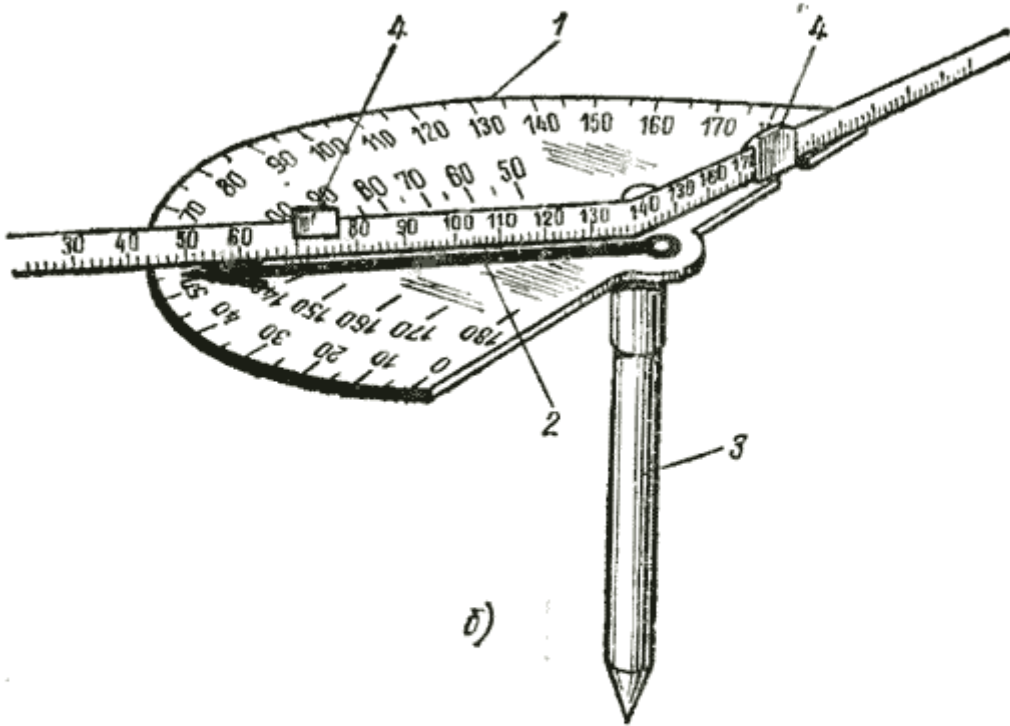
Набор инструмента и приспособлений типа НИЗ для замерщиков
